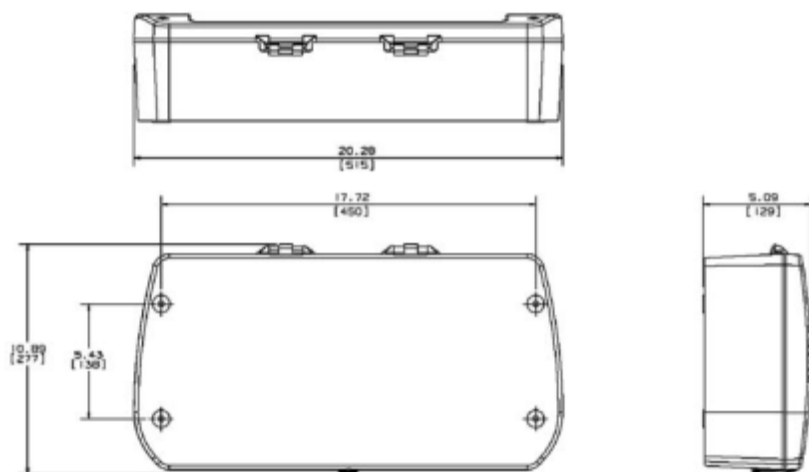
Schéma de montage [dimensions en pouces (mm)]
